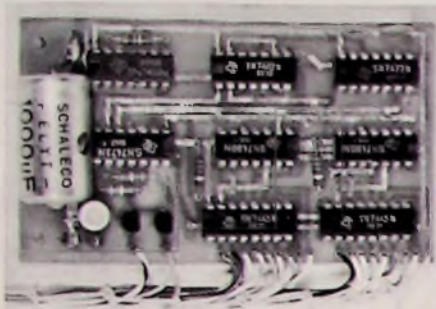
Der Ringzähler als gedruckte Schaltung (Abmessungen 94 mm x 56 mm)
